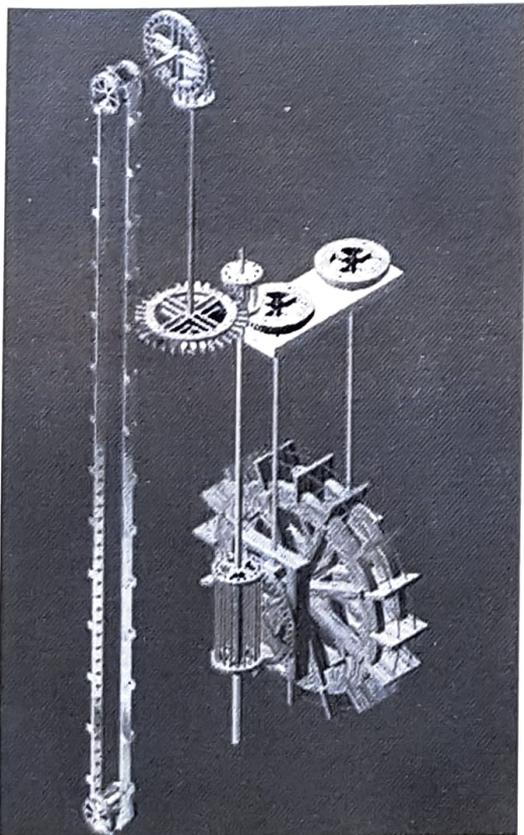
Esquema general de la segunda elevación. Plano del proyecto de reconstrucción del equipo de García-Diego.
